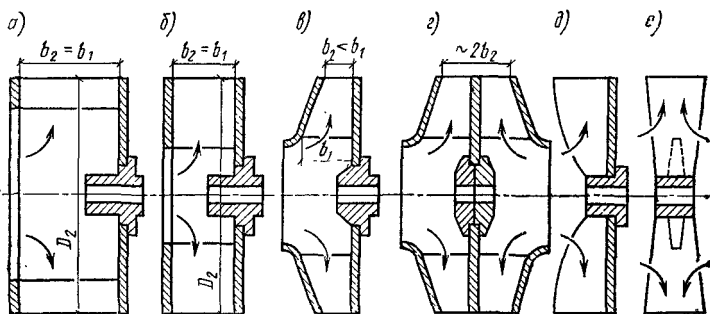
Конструктивные исполнения рабочих колес радиальных вентиляторов
